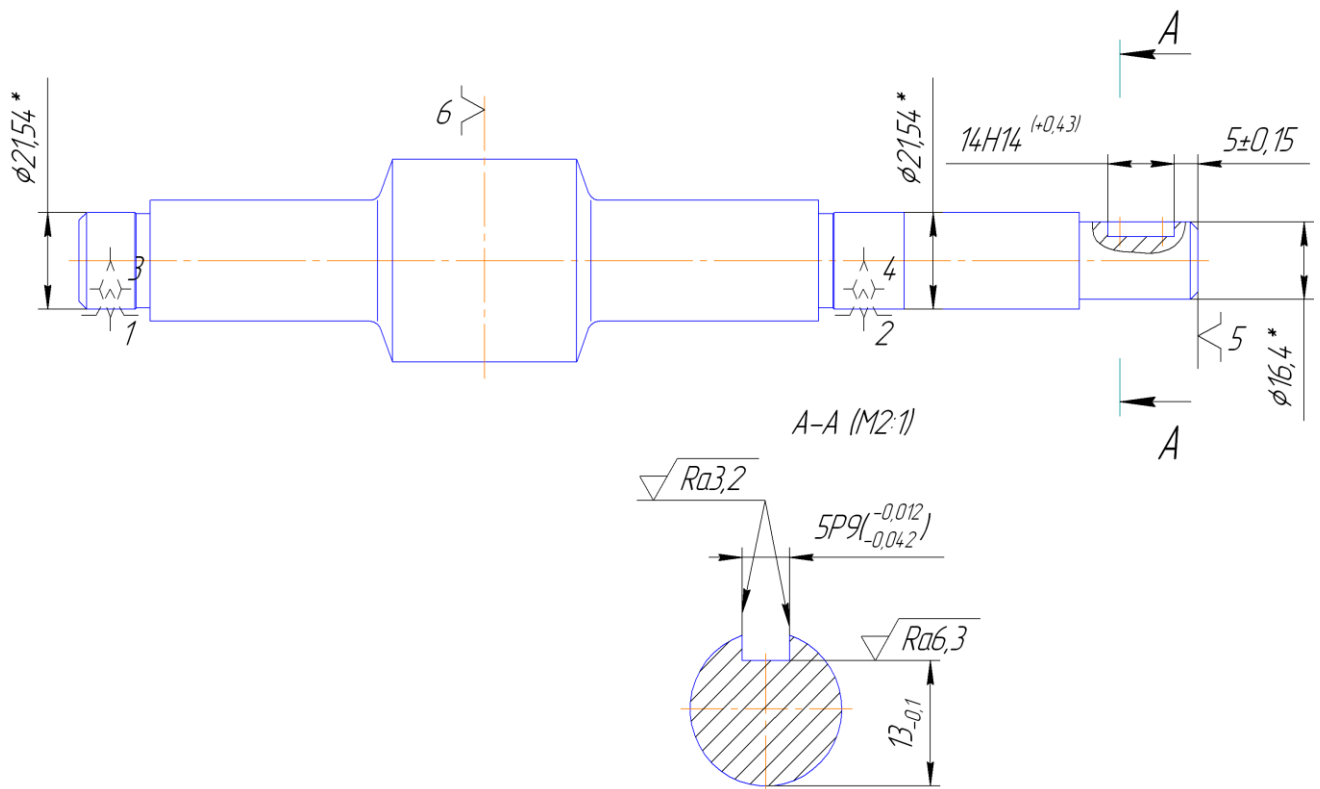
Ескіз на фрезерування паза 5P9 ( ${}_{-0,042}^{-0,012}$ ) в черв'яку ЧР211.03.14
